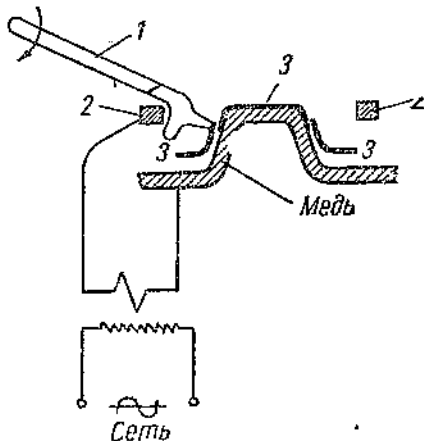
Установка для точечной сварки с переносными клещами.
